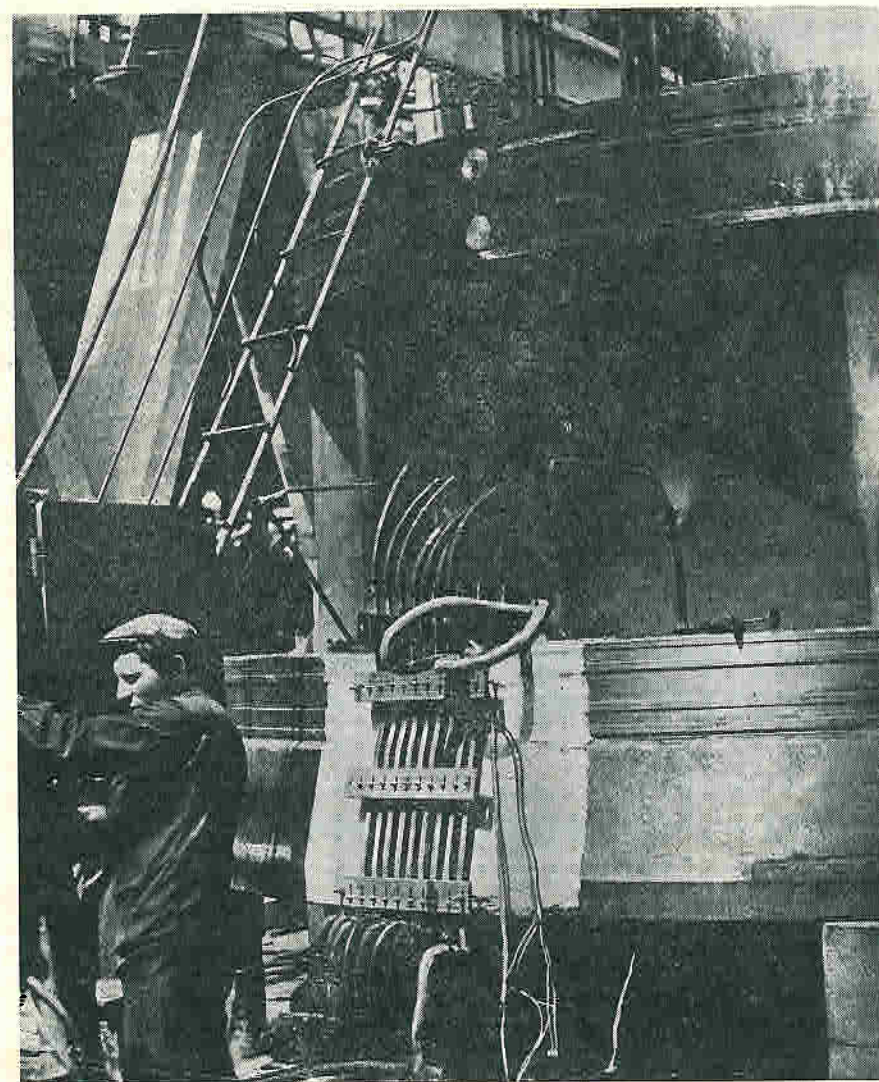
Термическая обработка индуктором сварного шва рабочего колеса гидротурбины Братской ГЭС
